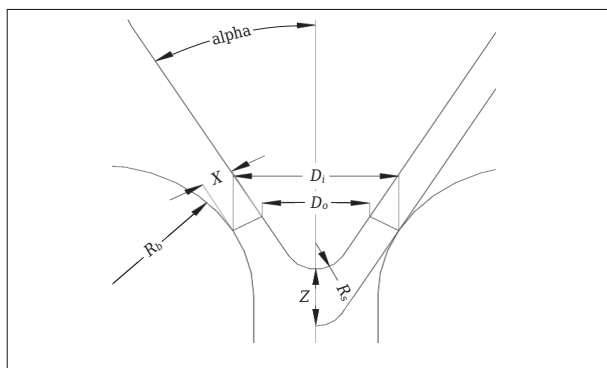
Схема обозначения размеров стопорной пары (стопор-моноблок и стакан-дозатор)
